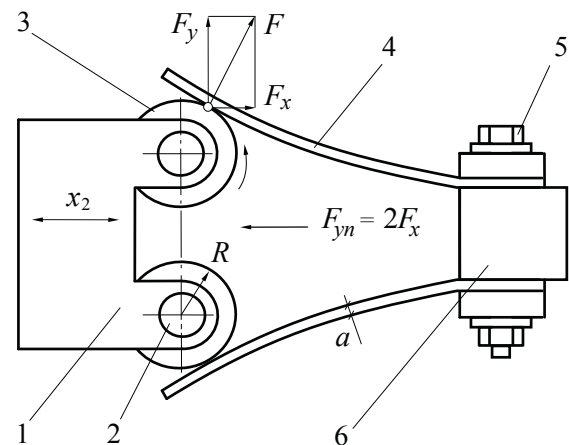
Нелинейный упругий элемент: 1 – корпус; 2 – оси; 3 – ролики; 4 – упругие пластины; 5 – резьбовое соединение; 6 – упор
